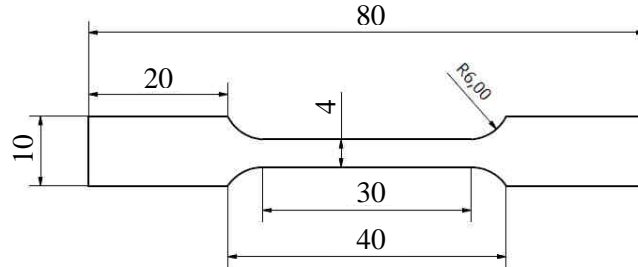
Géométrie de l'éprouvette de traction à chaud (côtes en mm)
